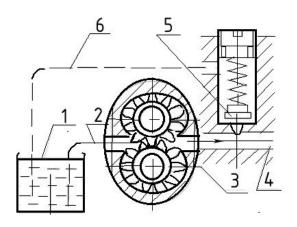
Схема шестерёнчатого насоса: 1 - масляный резервуар; 2, 6 - трубопровод; 3 - замкнутая камера насоса; 4 - нагнетательный трубопровод; 5-предохранительный клапан
